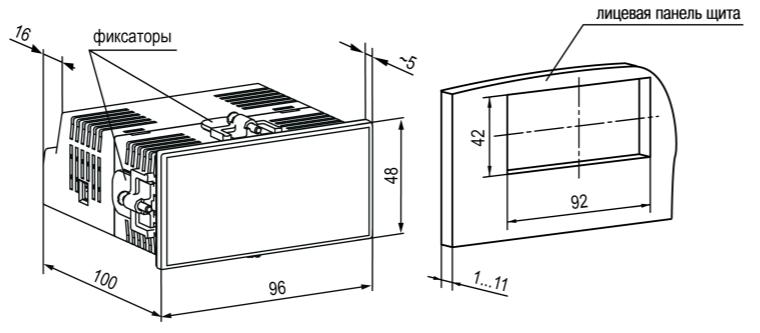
Габаритные размеры корпуса Щ2 и монтажного отверстия в щите
